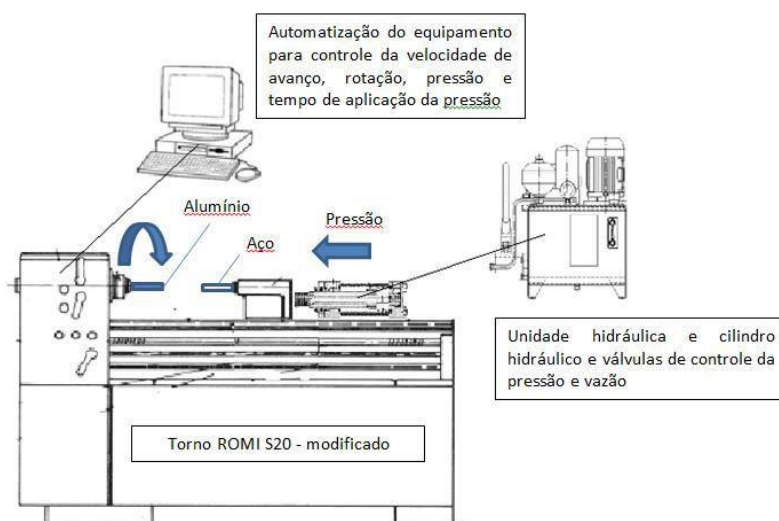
Torno mecânico ROMI S20 transformado em equipamento de solda por atrito rotativo
